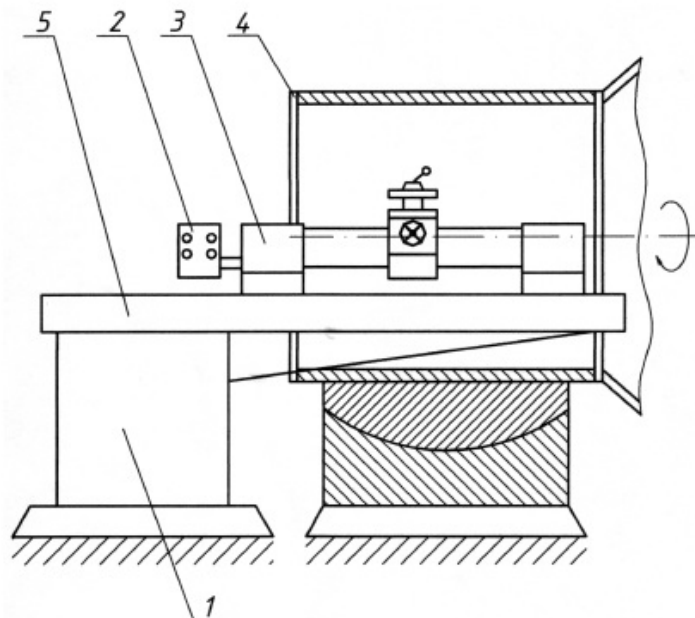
Схема установки специального приставного станочного модуля для обработки внутренней поверхности цапфы [17]:
